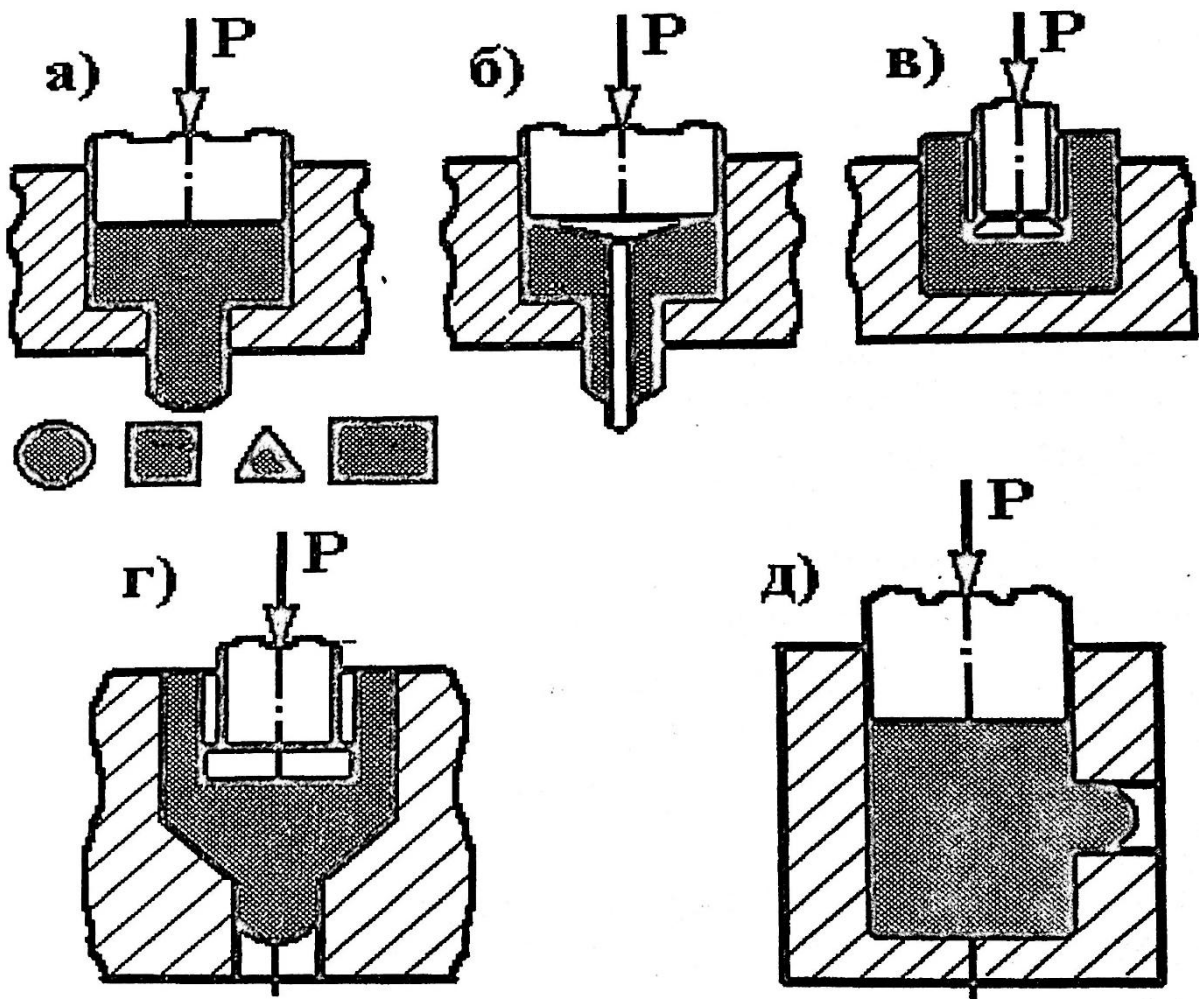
Схемы формообразования заготовки при холодном выдавливании
